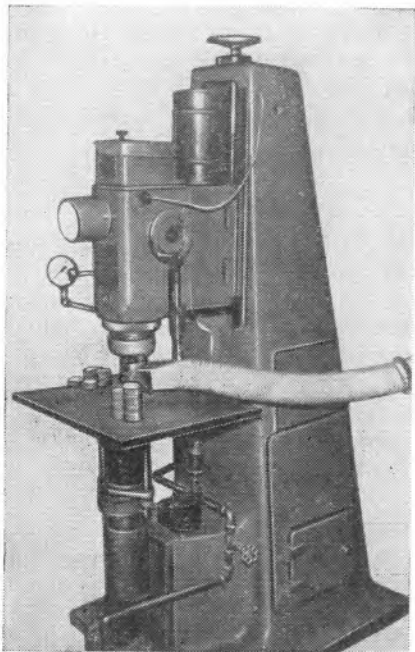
Пескоструйный прибор для определения твердости абразивных инструментов на керамической и бакелитовой связках зернистостью 50 и мельче
